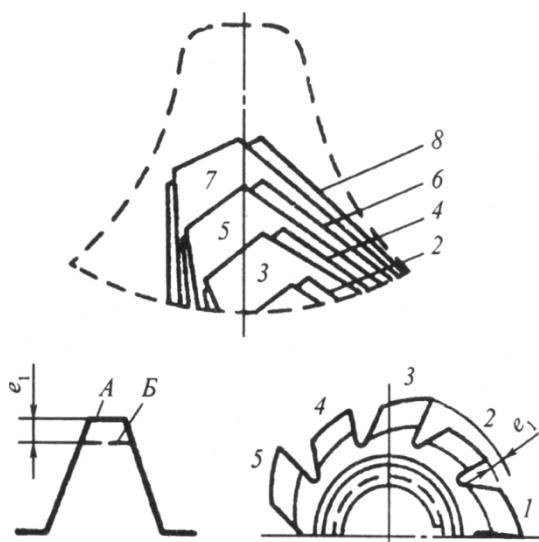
Последовательность срезания припуска во впадине колеса и профили зубьев фрез с вершиннонагруженной схемой резания: А – профиль зубьев с нечетными номерами; Б – профиль зубьев с четными номерами
